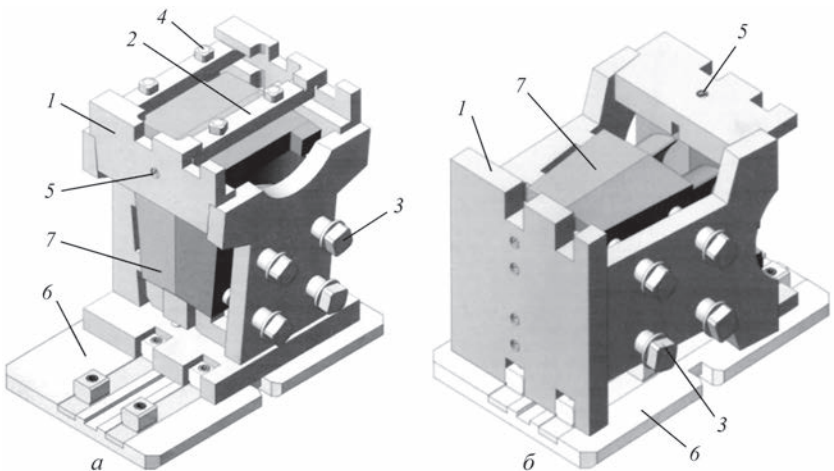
Пакети лопаток у оснащенні: а – положення для зварювання бандажної частини пакета; б – положення для зварювання хвостової частини пакета
